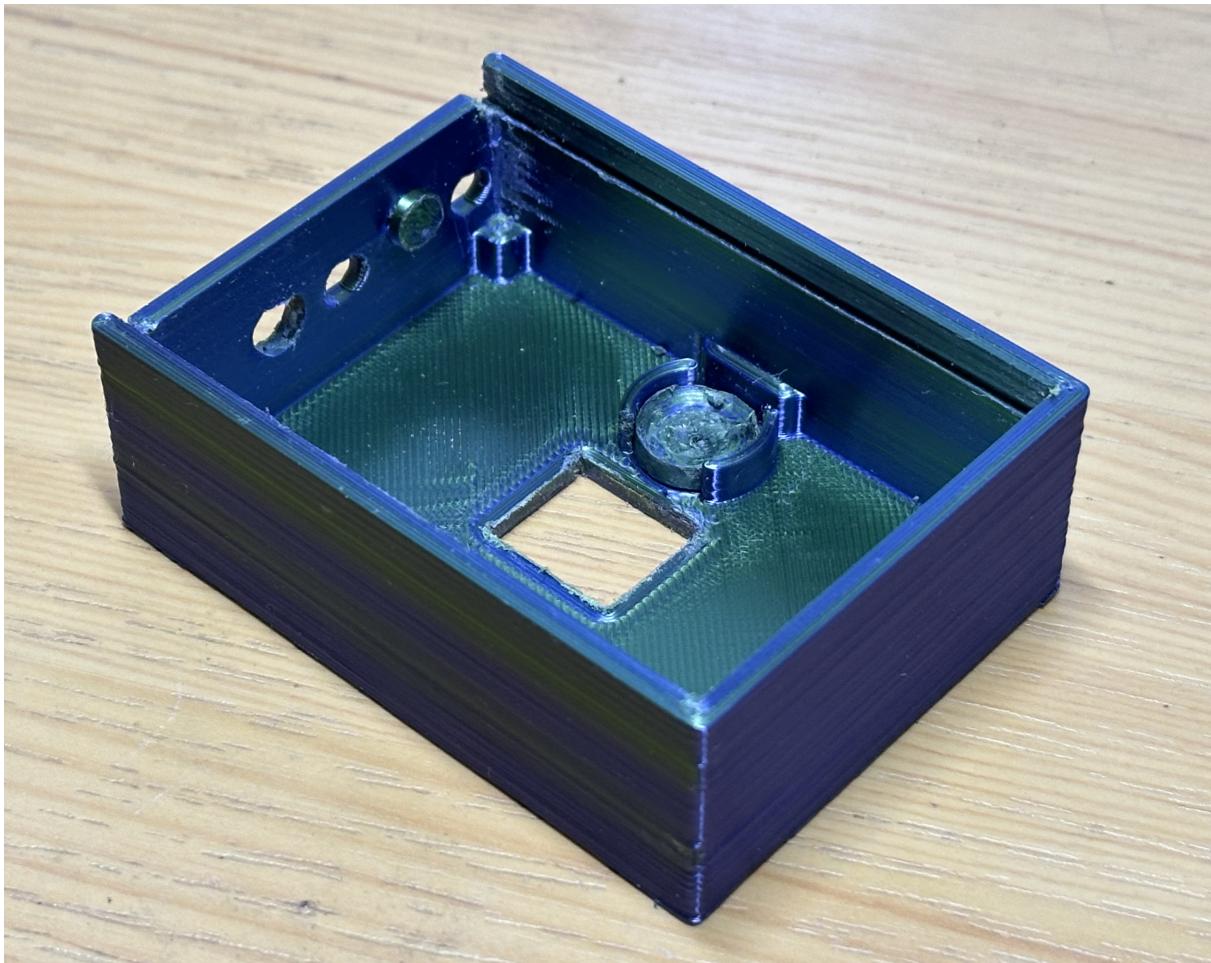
Корпус и кнопки, напечатанные на 3D-принтере
